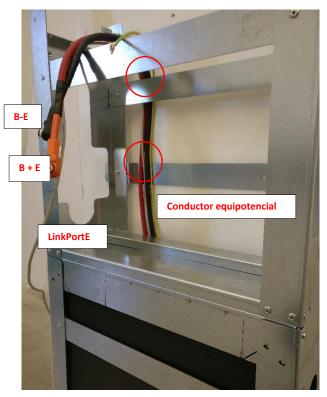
Tendido de conductores de conexión entre WALL-BOX-Bx BASE y WALL-BOX-Bx EXPANSION
